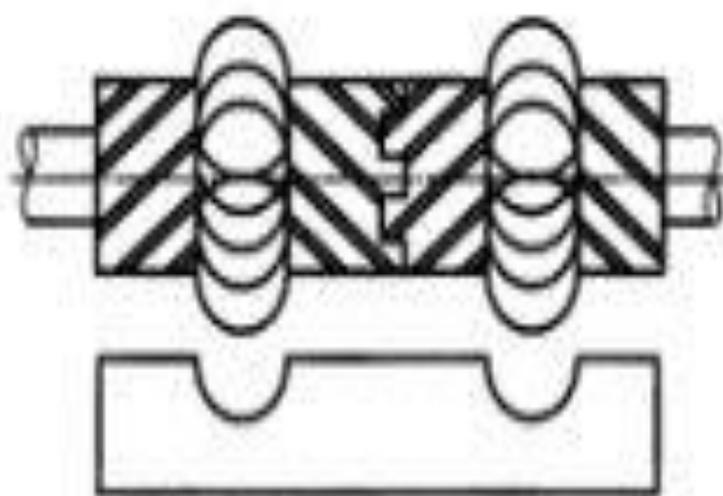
Фрезерование фасонной поверхности [autowelding.ru](http://autowelding.ru)
